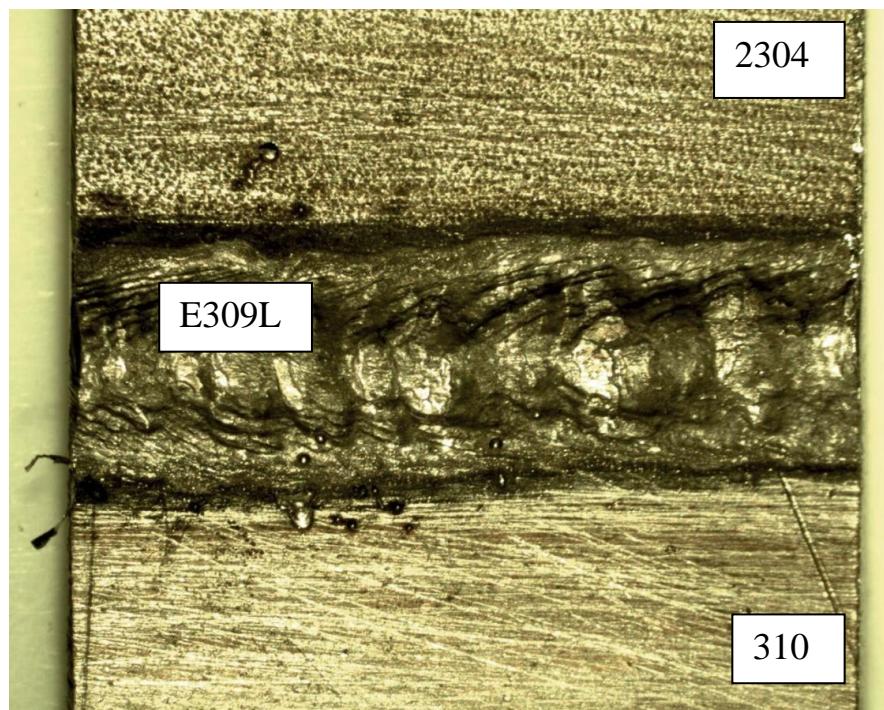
União das chapas de aço 310 com aço duplex 2304 com arame de adição 309L após processo de soldagem
